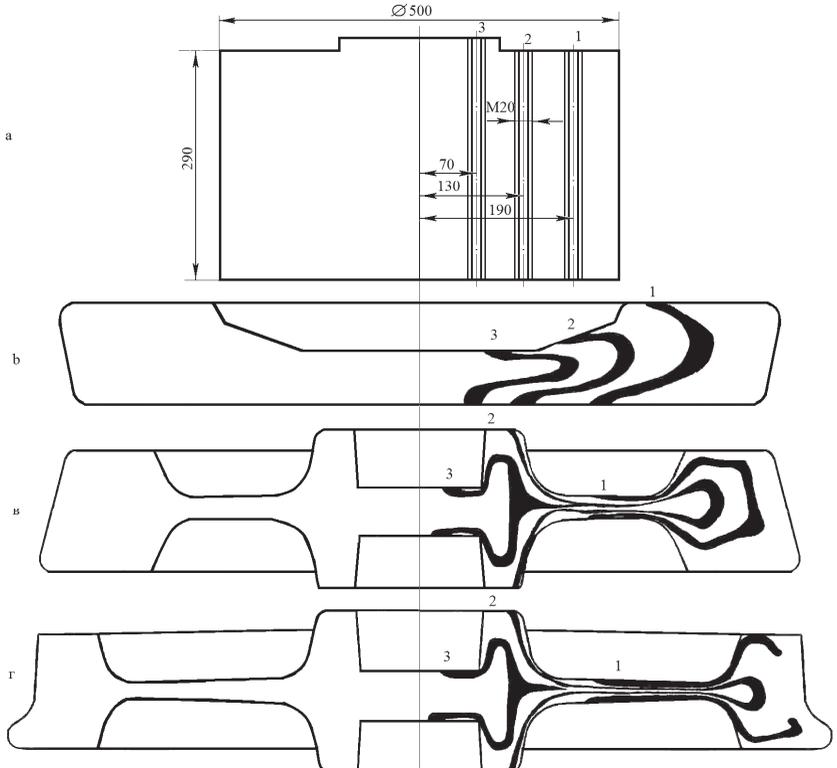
Схема течения металла при деформировании заготовки при изготовлении вагонных колёс: *a* - разрез исходной литой заготовки с вмонтированными в нее шпильками; *b* - *z* - заготовки со шпильками после соответственно осадки и разгонки, формовки, прокатки
